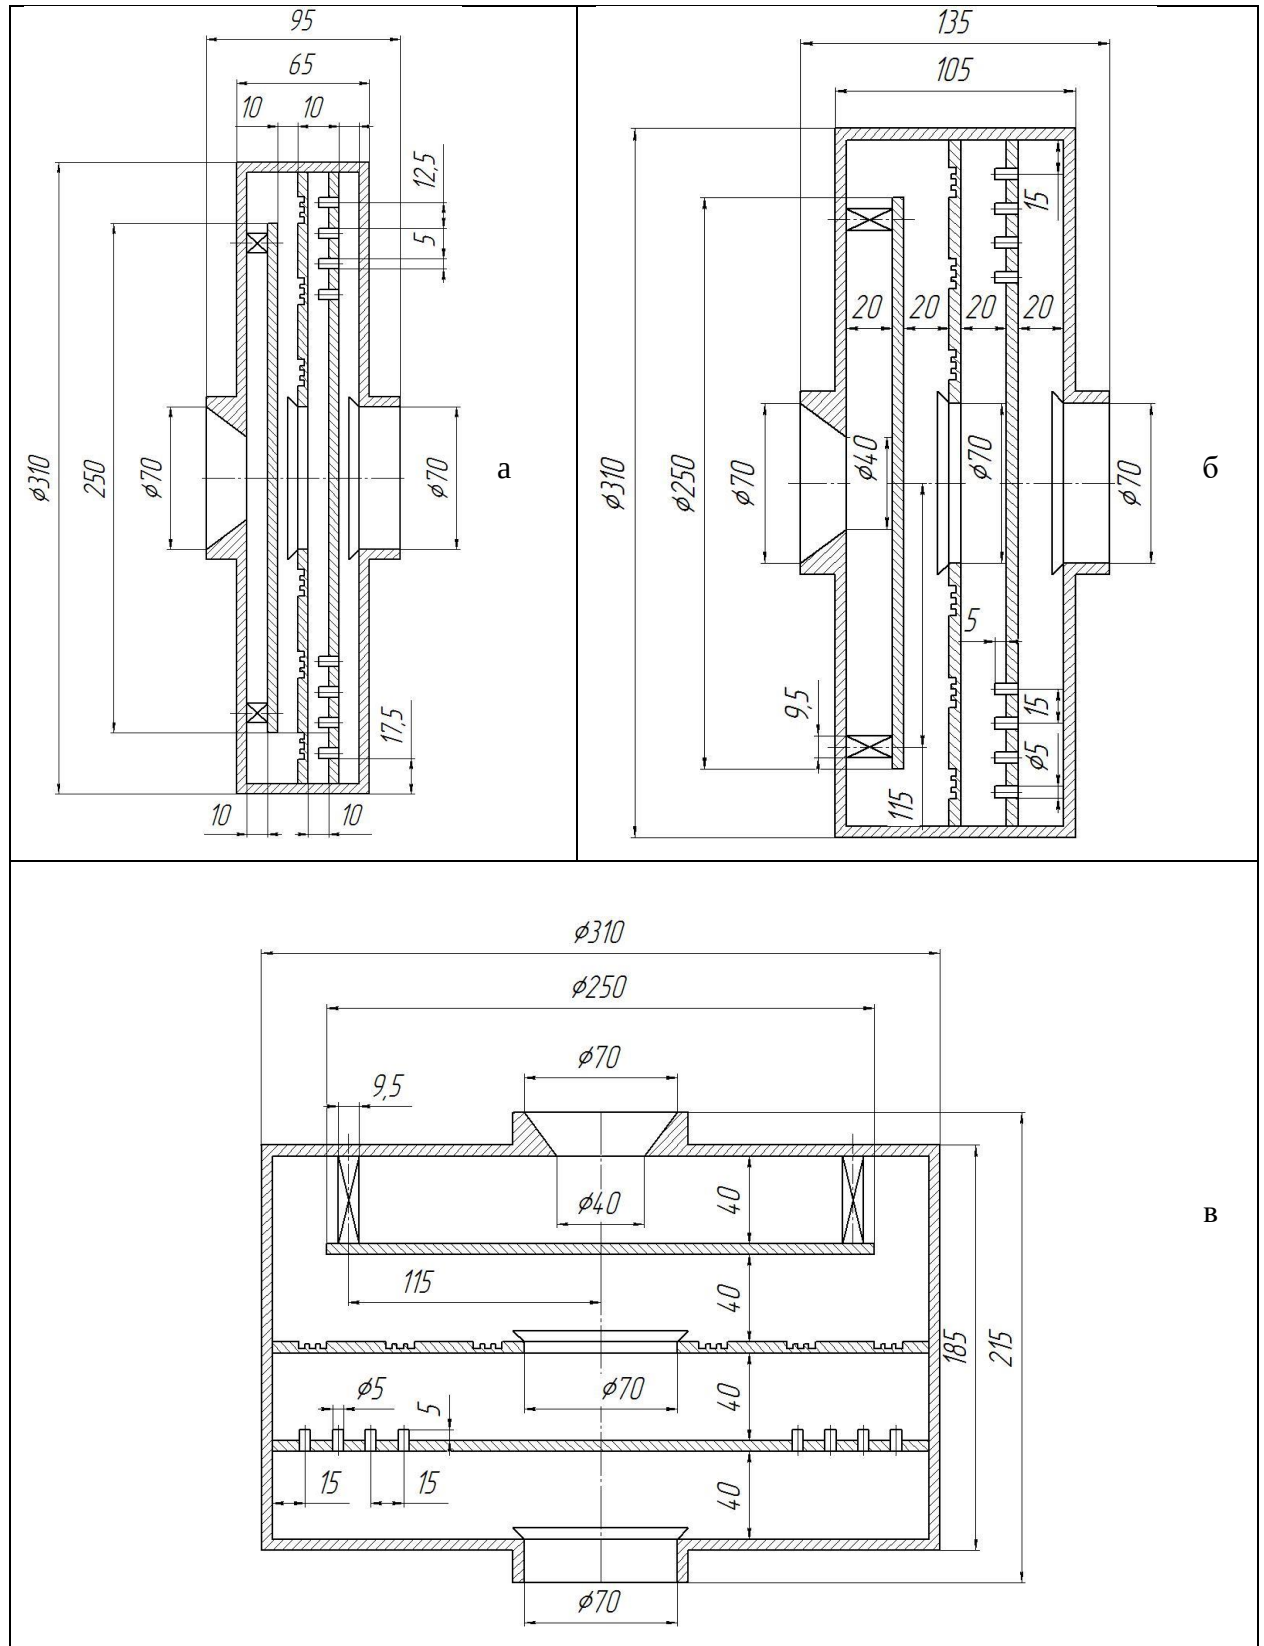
Робоча геометрія сепаратора паливного газу. Конструктивна схема 2. Розмір ступеня попередньої очистки:
